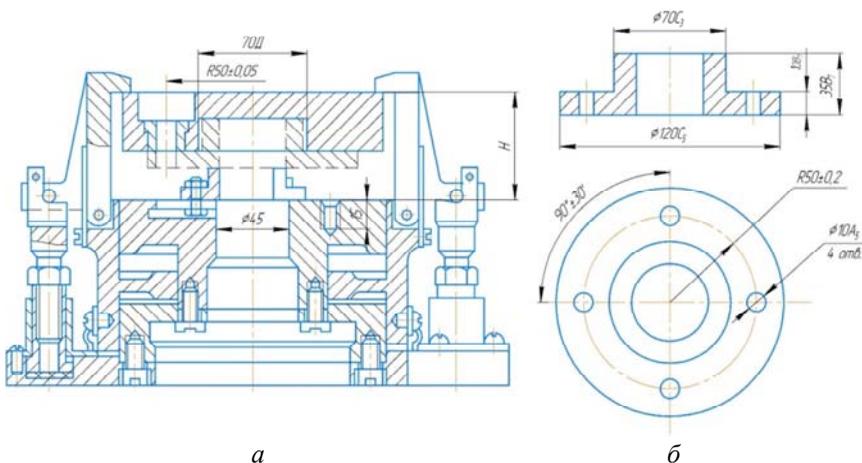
Унифицированный переналаживаемый кондуктор для сверления отверстий, расположенных в осевом направлении, во фланцах, дисках и втулках (а) и обрабатываемая деталь (б)
